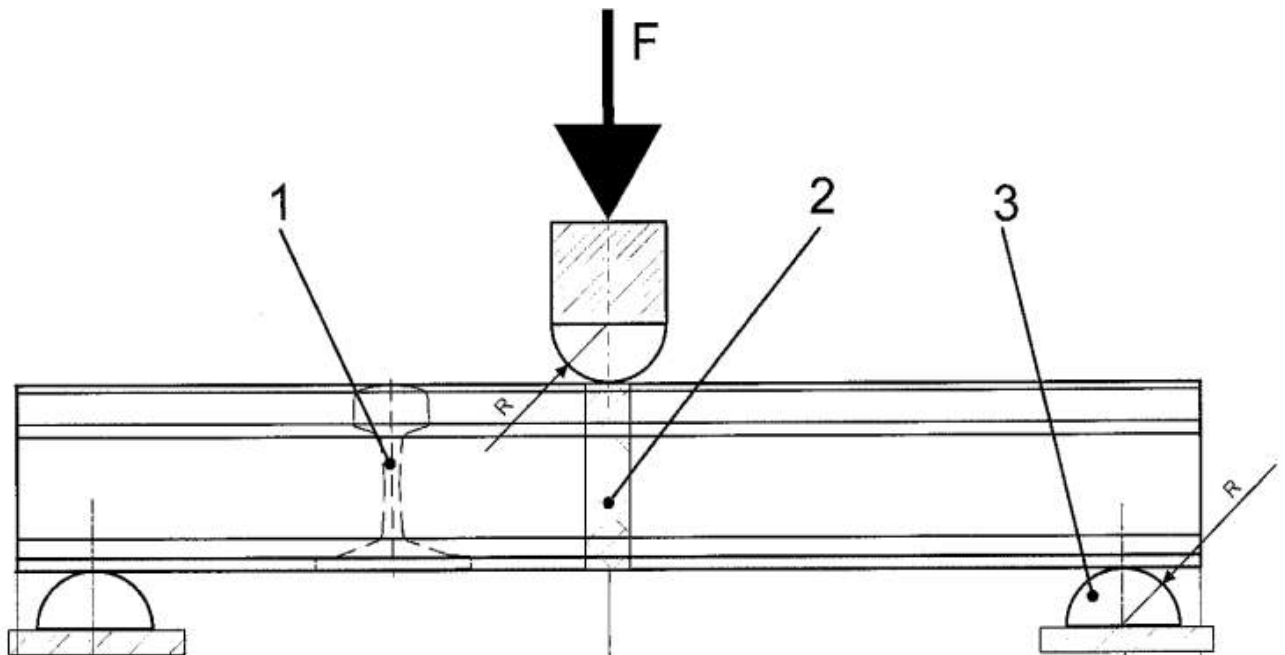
Схема випробування зварного стику рейок на статичний механічний згин: F - зусилля, 1 – переріз рейки, 2 - зварний стик, 3 - опора [97]
